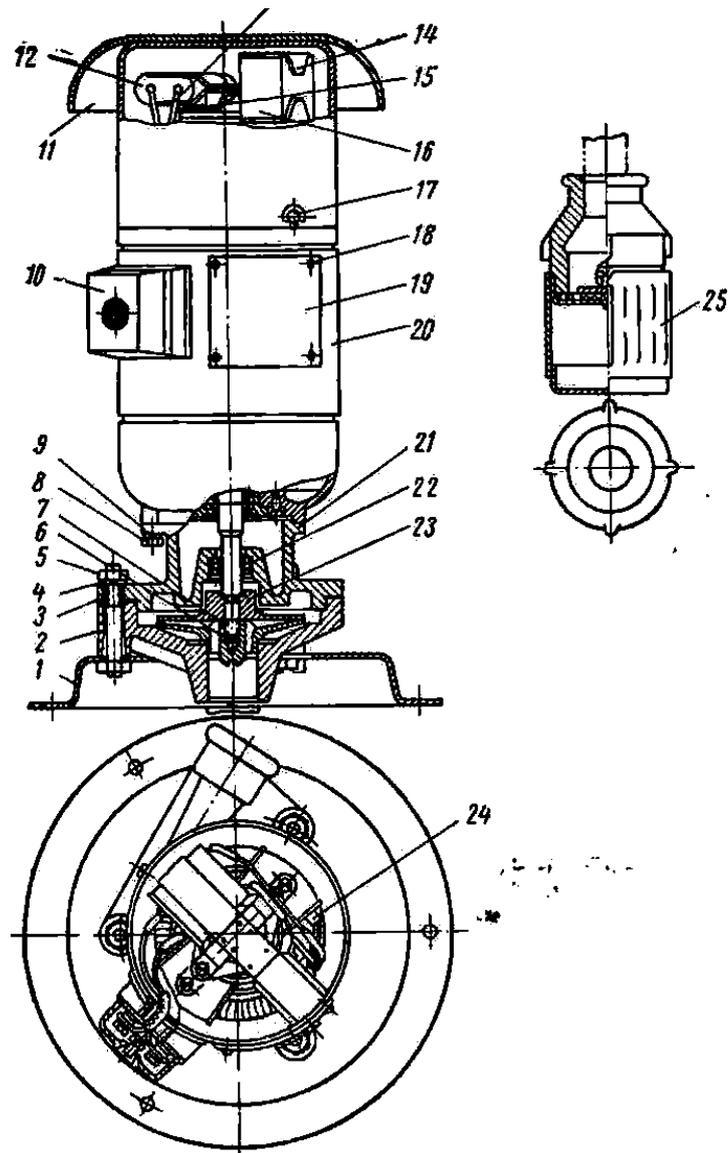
Электронасос «Кама»: 1- подставка; 2 - корпус; 3 - прокладка; 4, 7, 9 — шайба пружинная; 7 - гайка М8; 6 - гайка специальная; 8 - болт М6; 10 - коробка выводов; 11 - кожух; 12 - конденсатор; 13 - трубка; 14 - скоба; 15 - винт М4; 16 - конденсатор; 17 - винт специальный; 18- заклепка; 19 -
